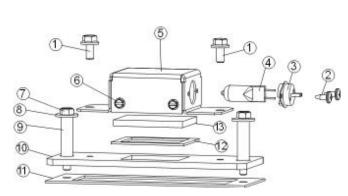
GF 160 DV IPI Ensemble de lampe d'accent
